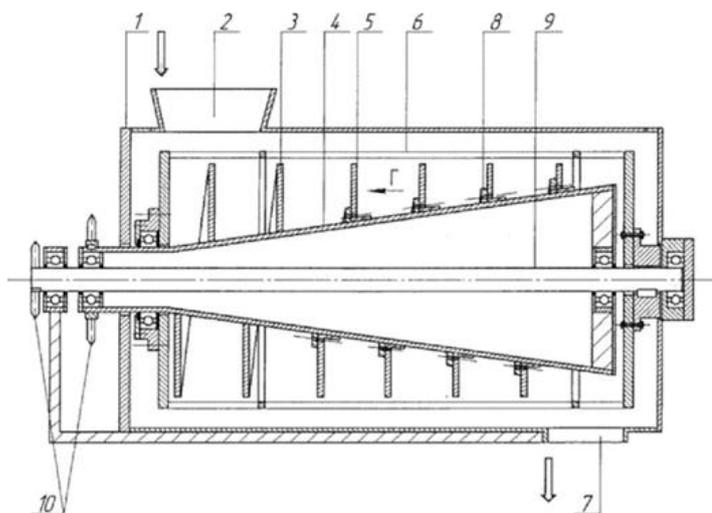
Схема измельчителя клубней картофеля: 1 - корпус; 2 - загрузочная горловина; 3 - шнек; 4 - конусный вал; 5 - нож; 6 - измельчающий барабан; 7 - выгрузная горловина; 8 - крепление ножей; 9 - вал привода измельчающего барабана; 10 - звездочки
